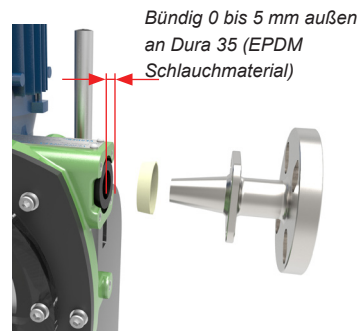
Schlauch bündig (Standard-Port Flansch)
